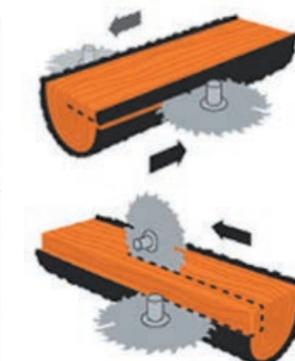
Схема работы станка с горизонтальными и вертикальными пилами
